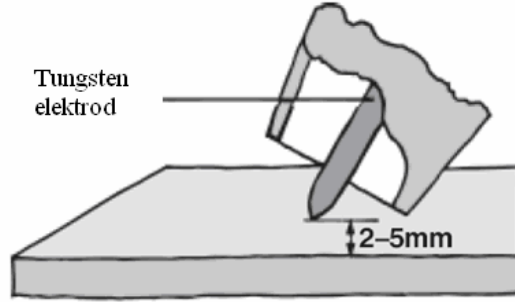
Dolgu metali kullanarak TIG kaynak uygulaması (Welder's Handbook, 1999).
